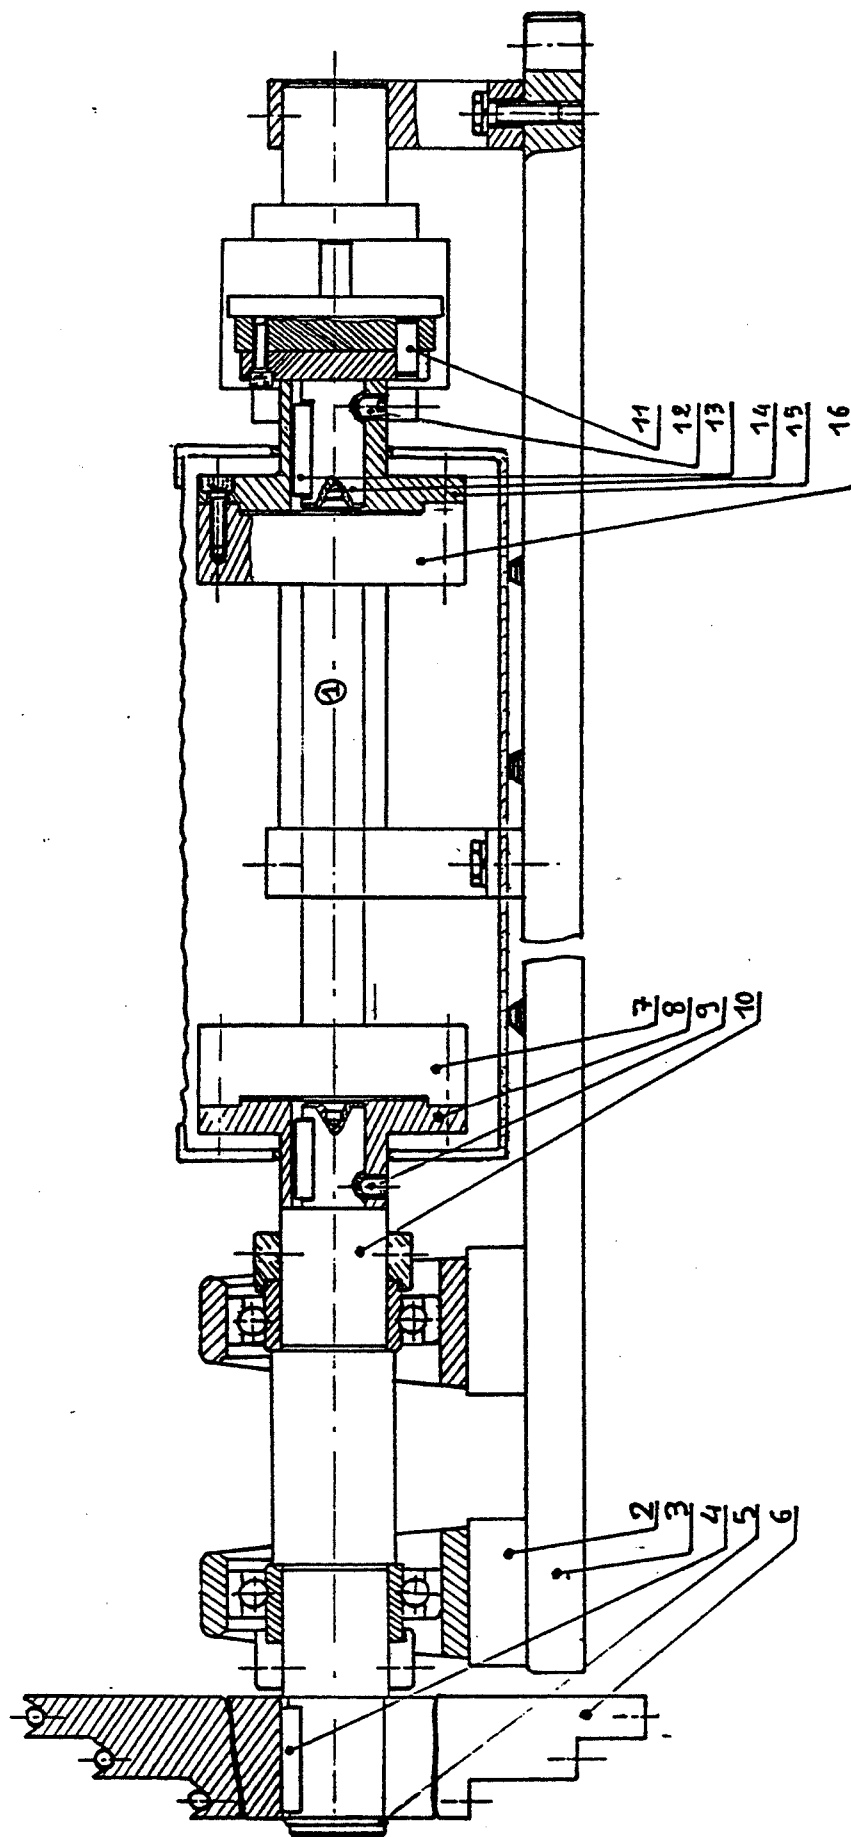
Dessin d'ensemble de la machine de torsion horizontale.
